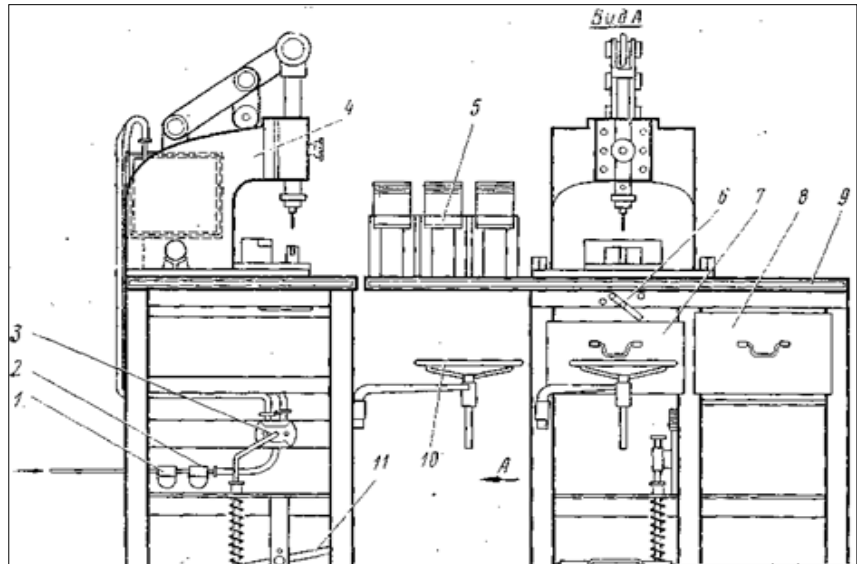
Механізований універсальний стенд для розбирання шатунно-поршневої групи двигунів:
